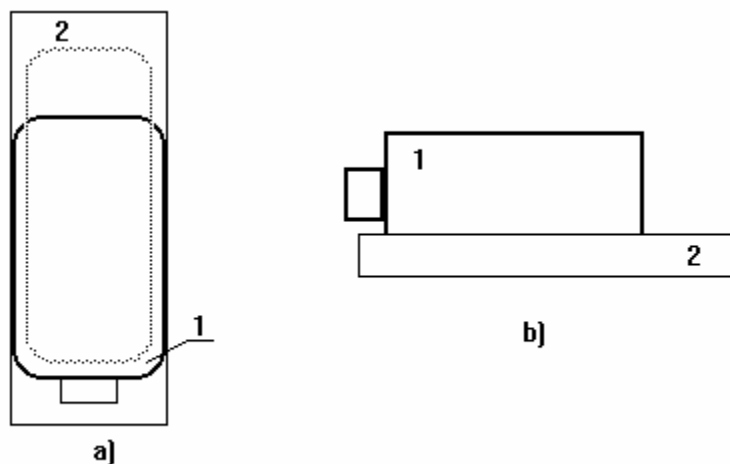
Способ создания стабильного зазора между преобразователем и поверхностью образца. а- вид сверху, b - вид сбоку, 1- преобразователь, 2 - прокладка.
